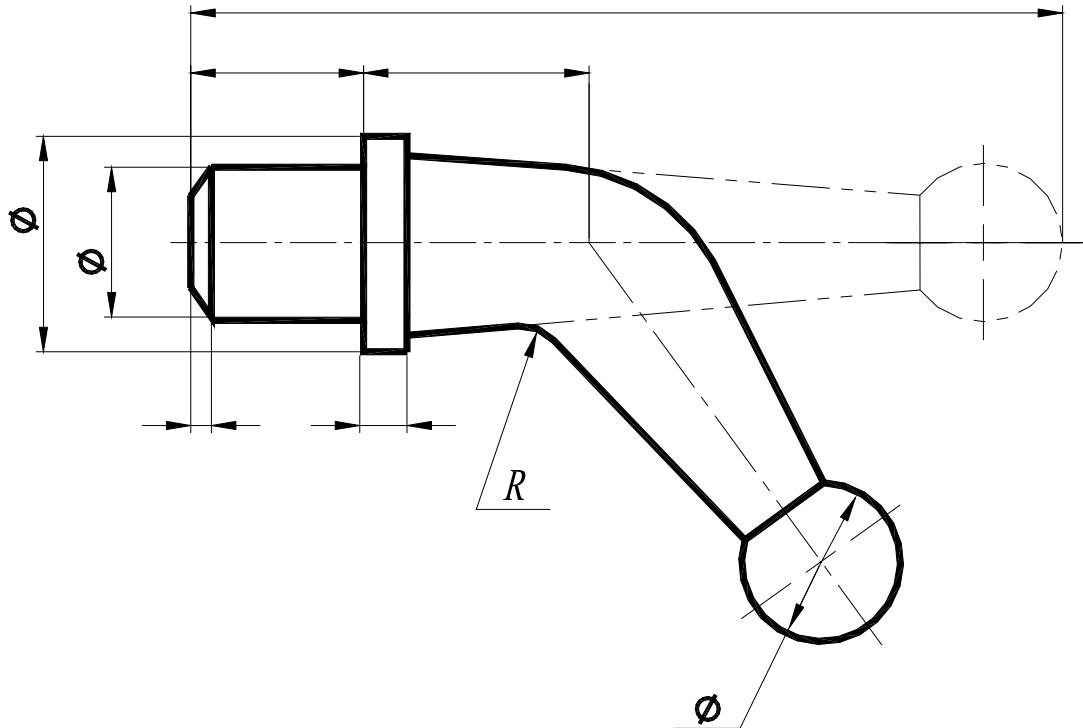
Пример нанесения размеров гнутой детали с частичной развёрткой
